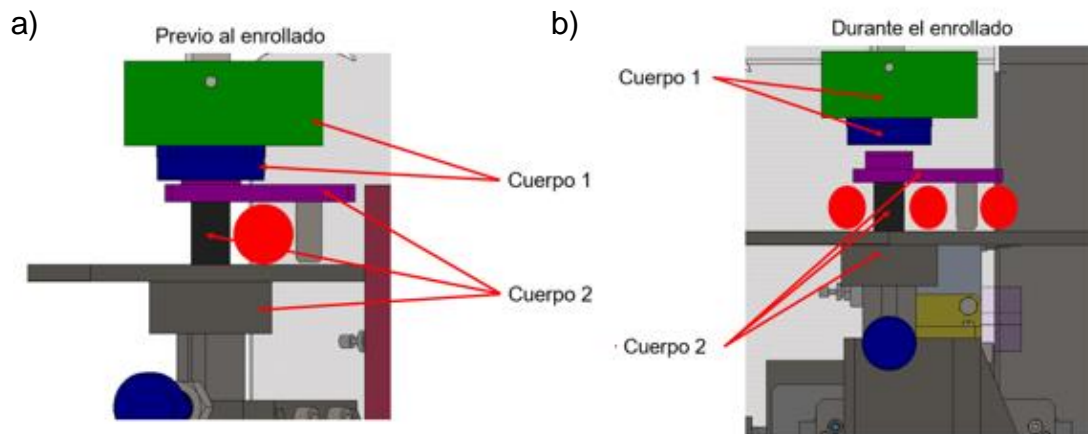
Posibles posiciones de la chistorra después del proceso de enrollado.
